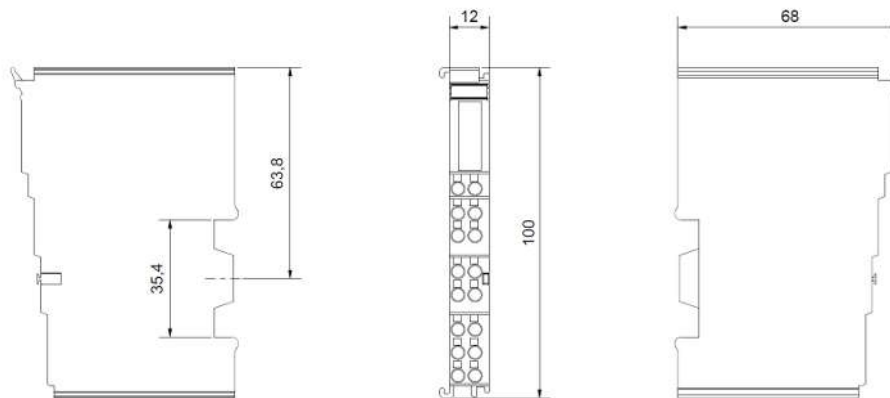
Technische Zeichnung | Gehäuse EL-12-16pin
